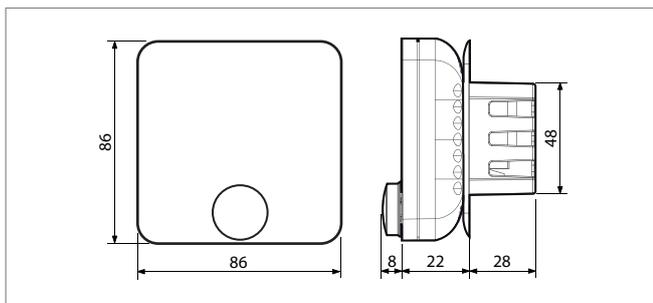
Dimensions pour l'élément de commande zone en cas de montage encastré (dimensions en mm)
